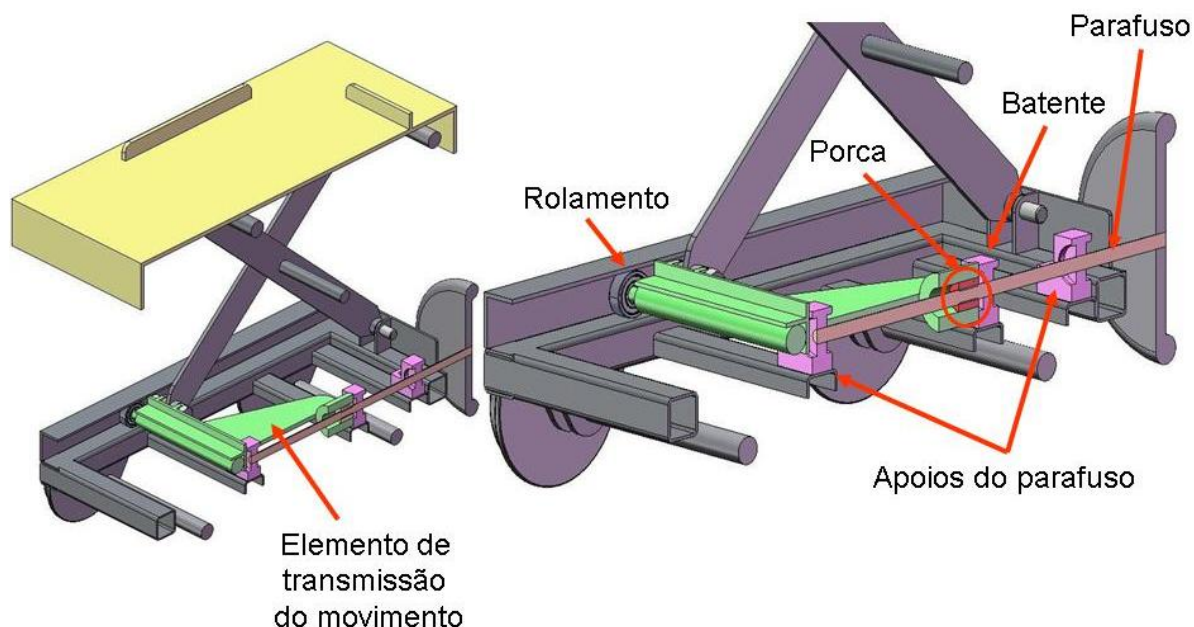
Vista em corte do sistema de parafuso para elevação da câmara de vazamento. Vista em pormenor, do sistema da porca.
